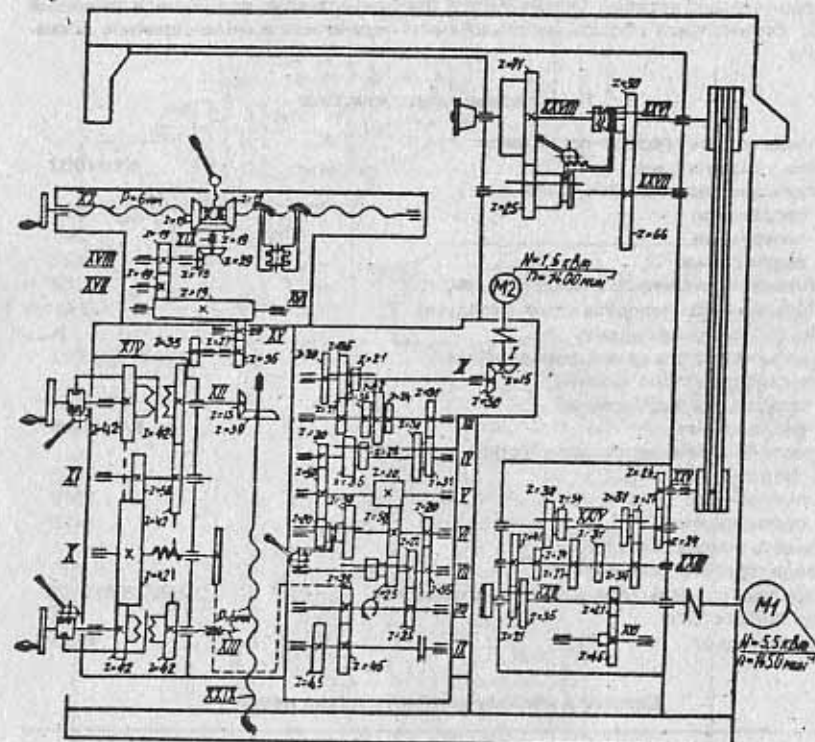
Кинематическая схема универсально-фрезерного станка мод. 6Р81
